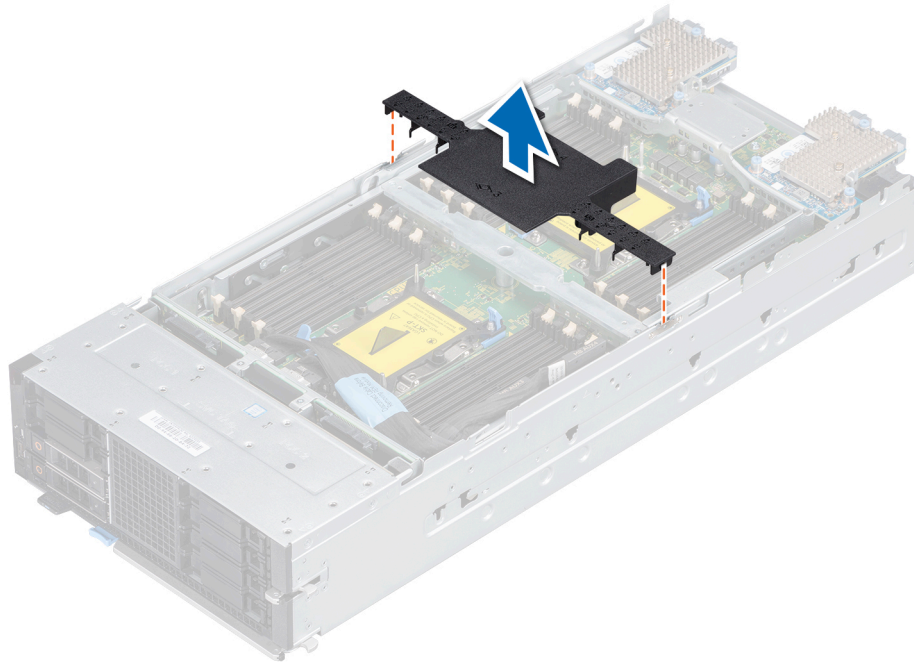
Entfernen des Kühlgehäuses vom PEM
